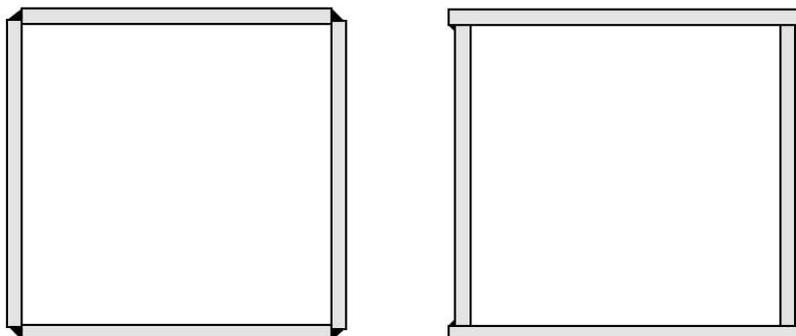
Geschweißte quadratische oder rechteckige Hohlprofile
